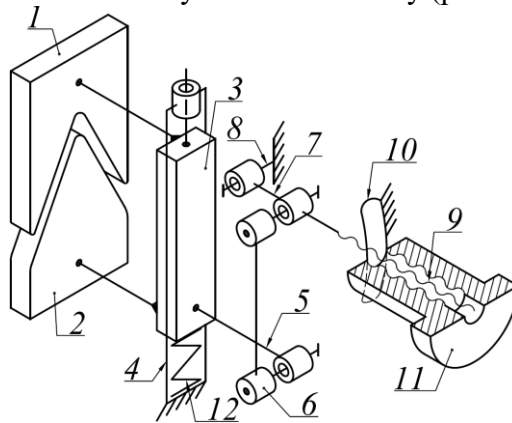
Конструктивна схема механізму зміни глибини кулірування
